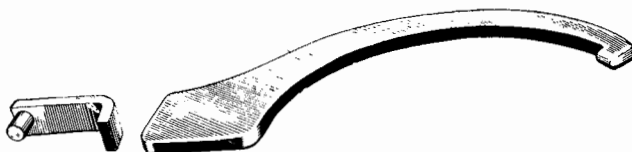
Ключ 48001-1-020МД к гайке дет. 233-15-104 ведущего колеса
